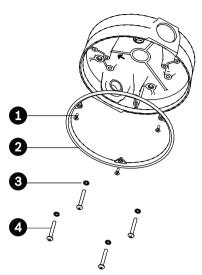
Colocação da junta circular e do anel de retenção para instalação exterior
